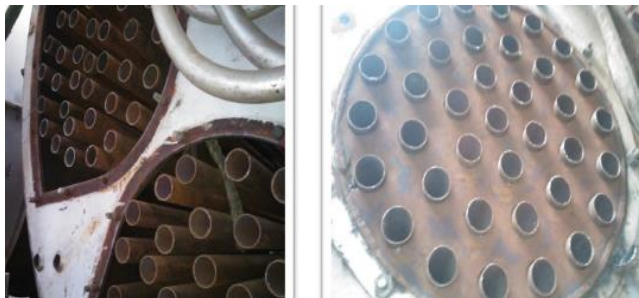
, 9.13 Montaje cañería, Soldadura en punta de cañerías.
